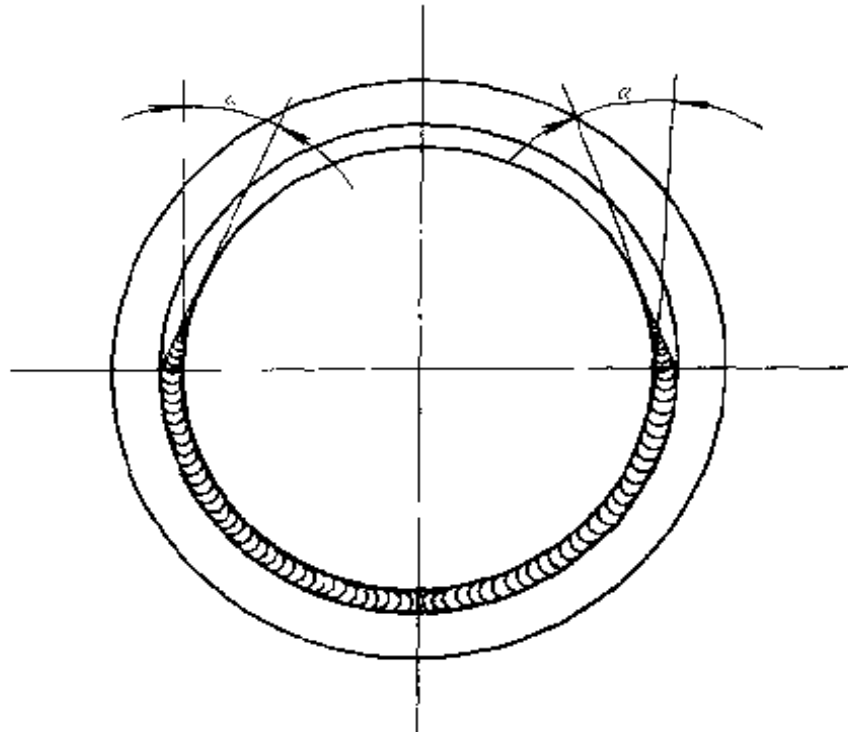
管对接垂直固定障碍焊焊缝接头处的修磨尺寸
